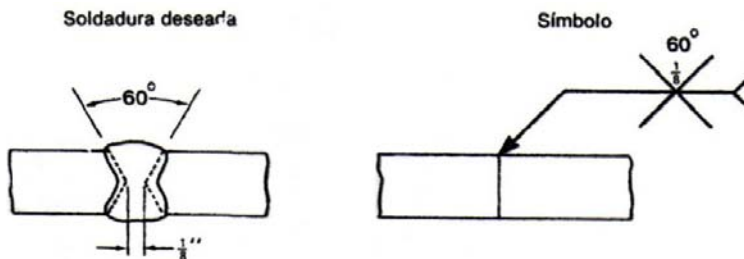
Símbolo de soldadura en el que se especifica una soldadura de doble ranura con ambas ranuras de las mismas dimensiones
